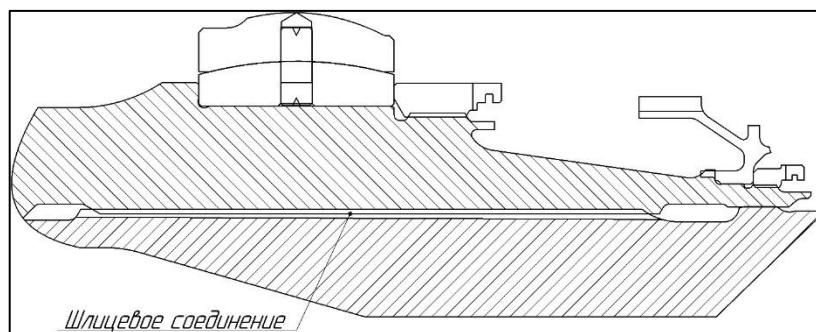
Шлицевое соединение роторов КНД и ТНД двигателя GE 90
